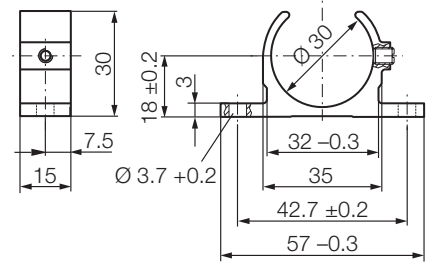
Befestigungsklammer BTL6-A-MF01-A-43
